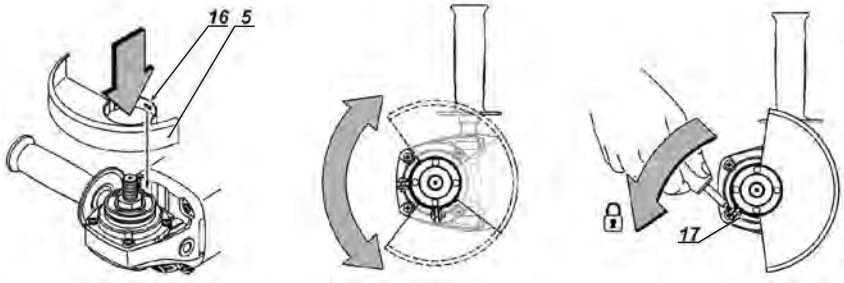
Montaje y posicionamiento de la tapa de protección
